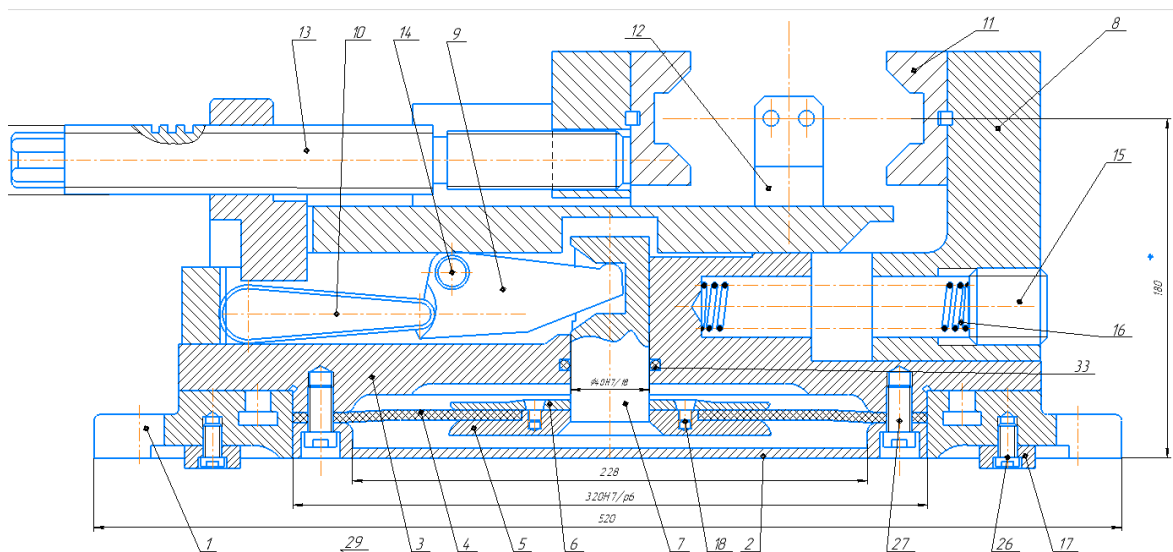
Тиски пневматичні: 1 – плита; 2 – кришка; 3 – корпус; 4 – мембрана; 5,6 – шайба; 7 – шток; 8 – ползун; 9 – ричаг; 10 – штовхач; 11 – призма; 12 – упор; 13,18 – винт; 14 – вісь; 15 – пробка; 16 – пружина; 17 – шпонка;
